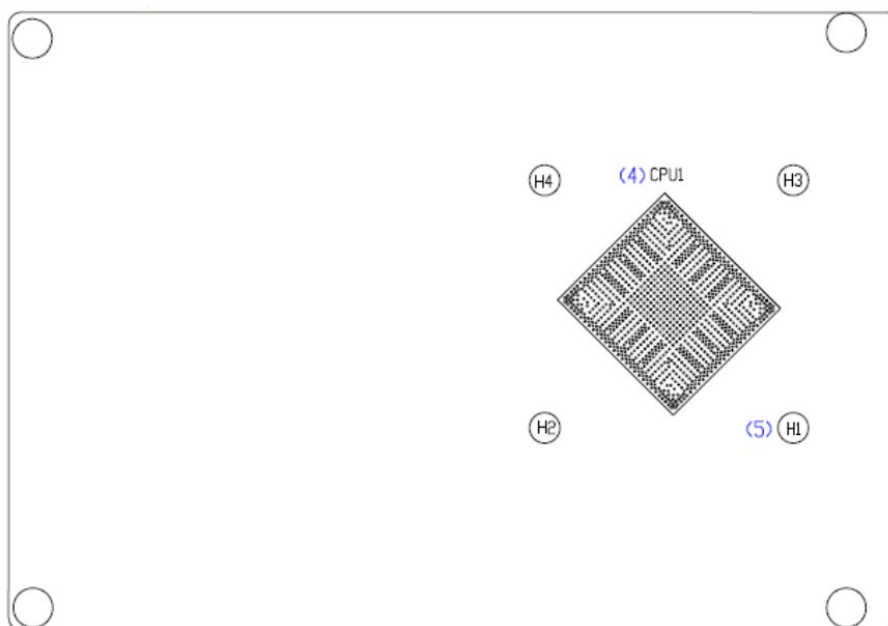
SBC-7116 - Anschlüsse und Jumper - Untersicht
